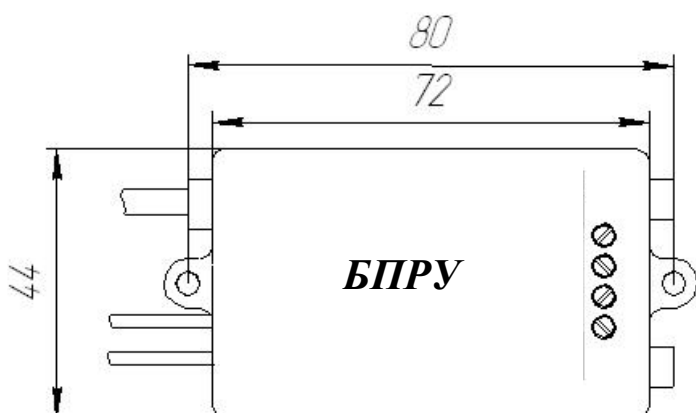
Габаритные и установочные размеры блока питания БПРУ-232 (БПРУ-485)
